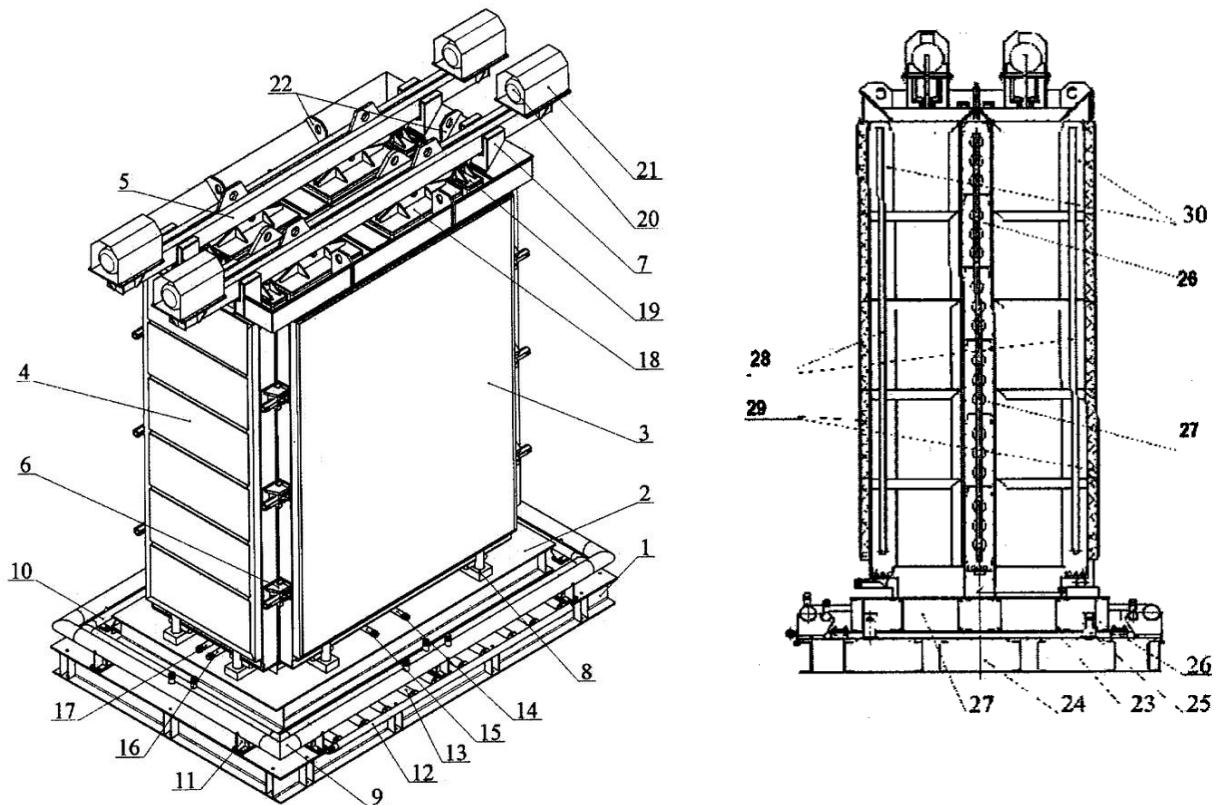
Стендова установка для виготовлення двох блоків:
